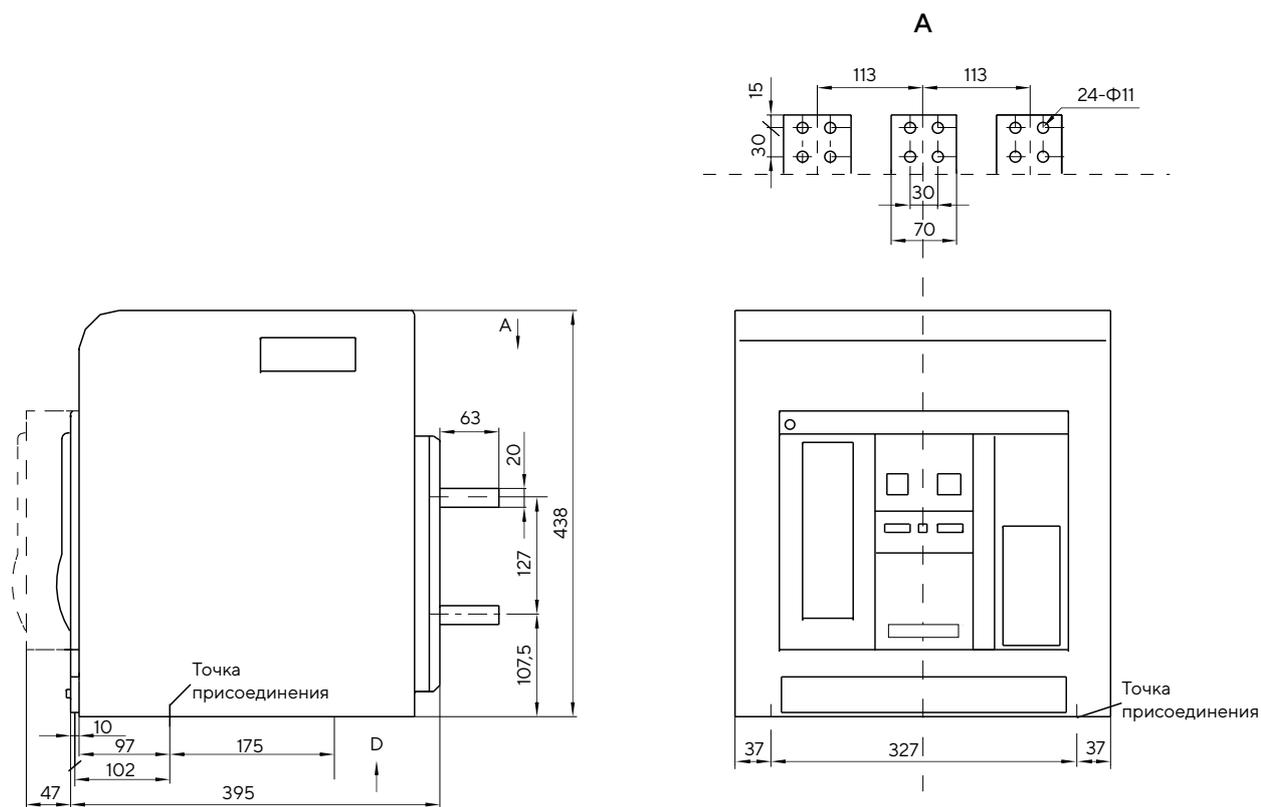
Габаритные размеры выдвижных трехполюсных выключателей типоразмера D
